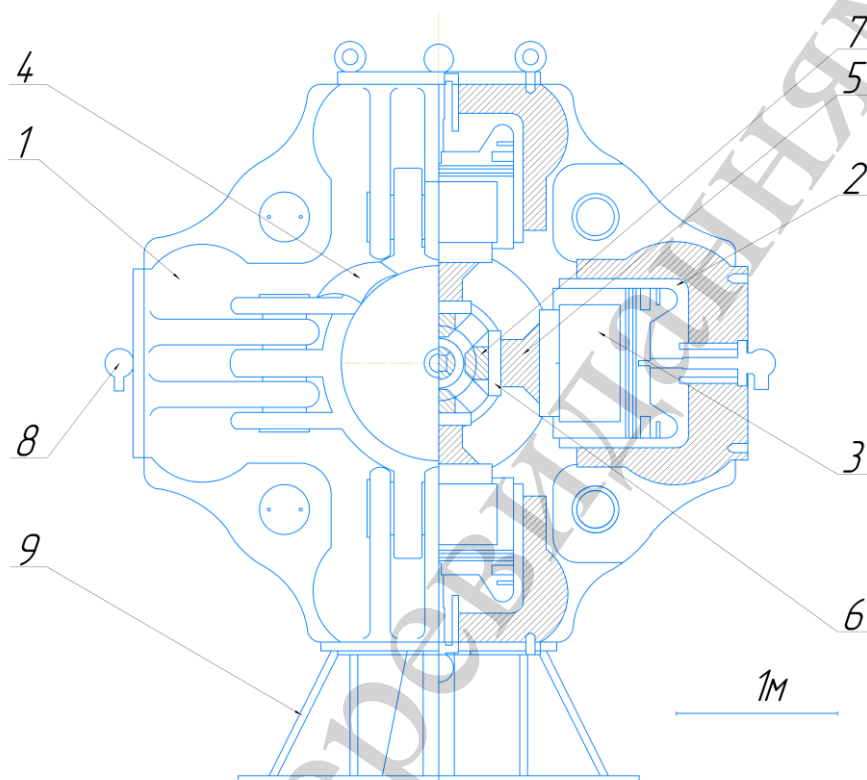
Общий вид пресса CS-VII[6]: 1 – станина пресса, состоящая из шести плунжерных деталей корпуса, обеспечивающих перемещение пунсонов в трех взаимоперпендикулярных направлениях; 2 – цилиндр для создания высокого давления рабочей жидкости (масло); 3 – поршень; 4 – защитный экран рабочего пространства; 5 – опорные плиты; 6 – охлаждающая обойма нажимного пуансона; 7 – твердосплавный пуансон; 8 – клапан для подачи масла; 9 – опорная стойка
